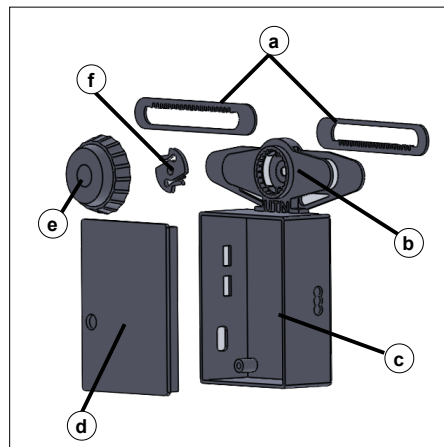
Vista explosionada del dispositivo inalámbrico.
